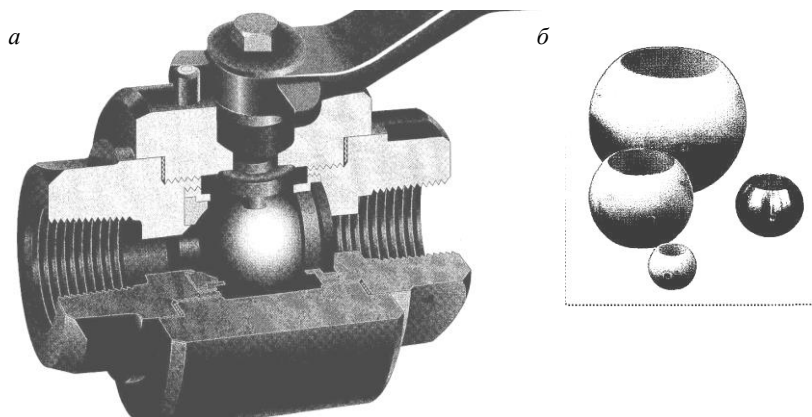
Шаровой кран (а) и шаровой герметизирующий элемент (б)
